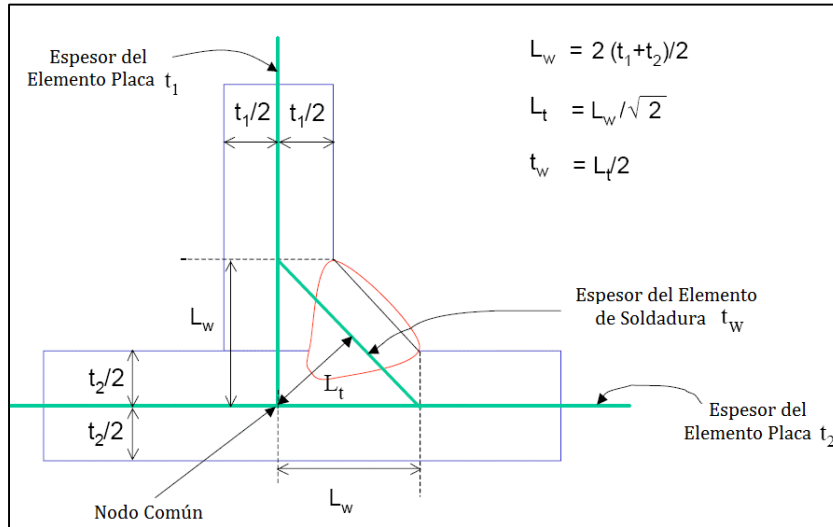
Modelado FEM Unión Soldada en "T" (Placas de Acero $t < 3$ mm) [29]
